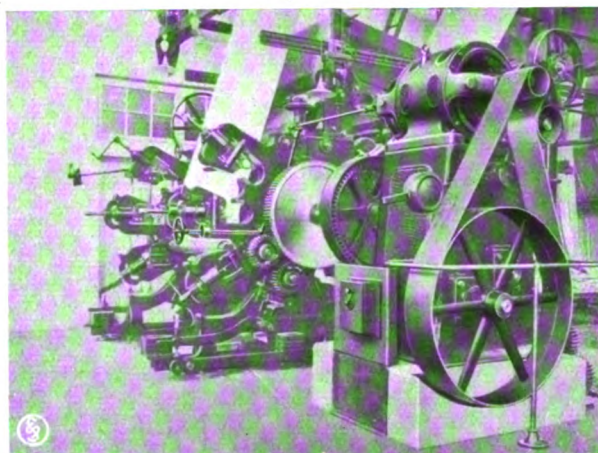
Achtfarben-Zeugdruckmaschine, angetrieben durch Drehstrom-Nebenschlußmotor mit Riemen und Spannrolle.
